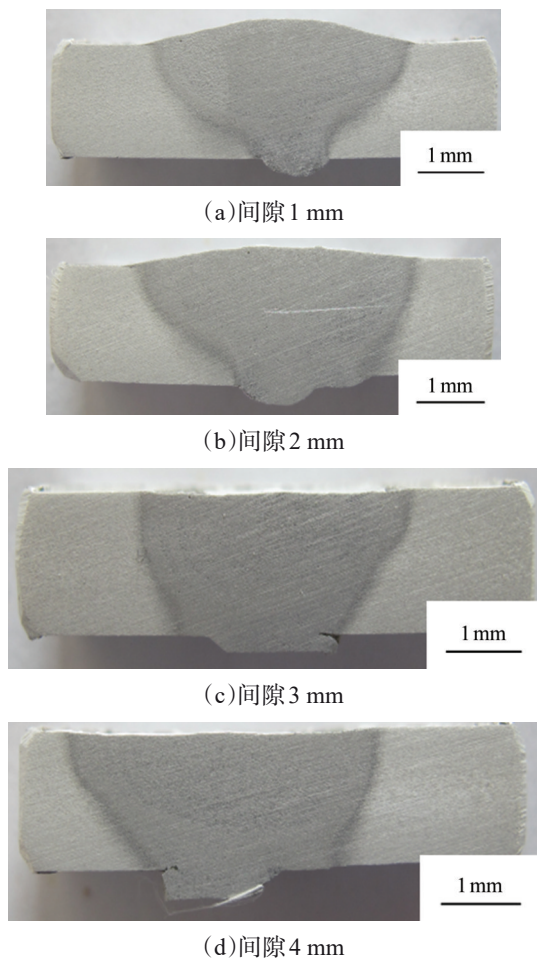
不同装配间隙下的焊接接头宏观形貌
